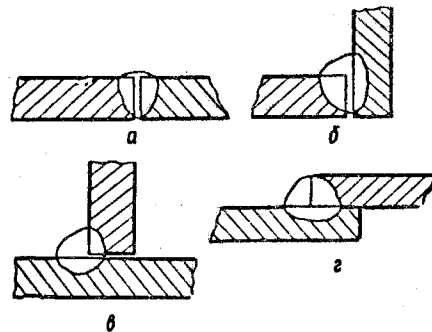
Виды сварных соединений: а — стыковое; б — угловое; в — тавровое; г — нахлесточное
